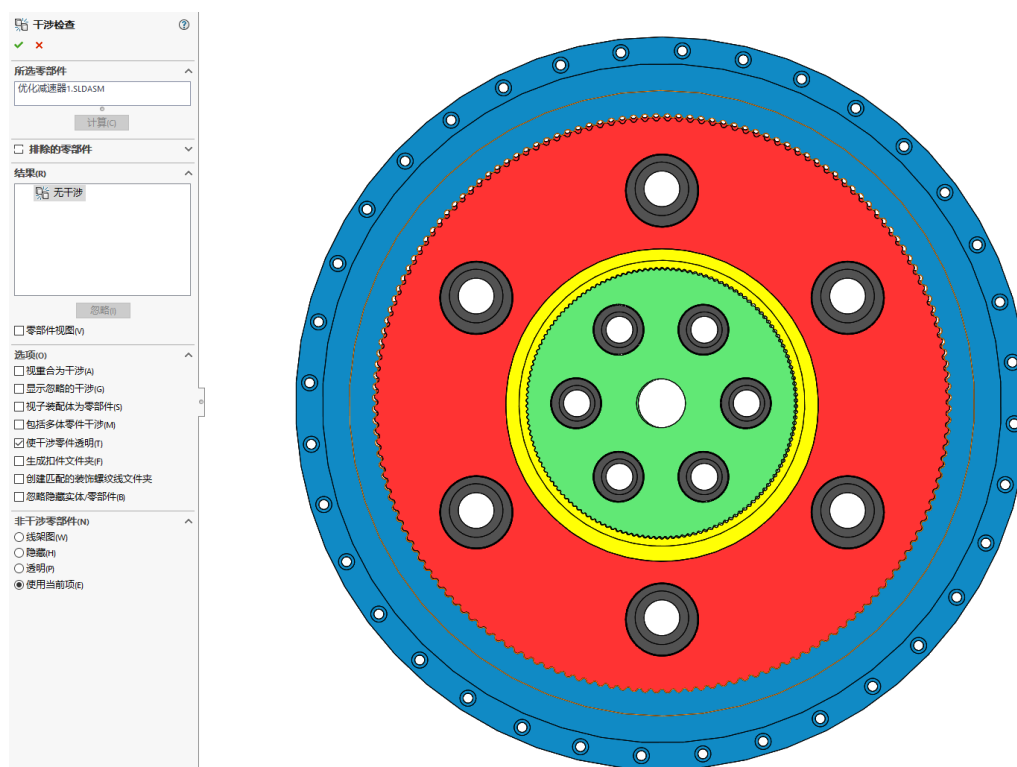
Обнаружение помех на узле редуктора в SolidWorks
